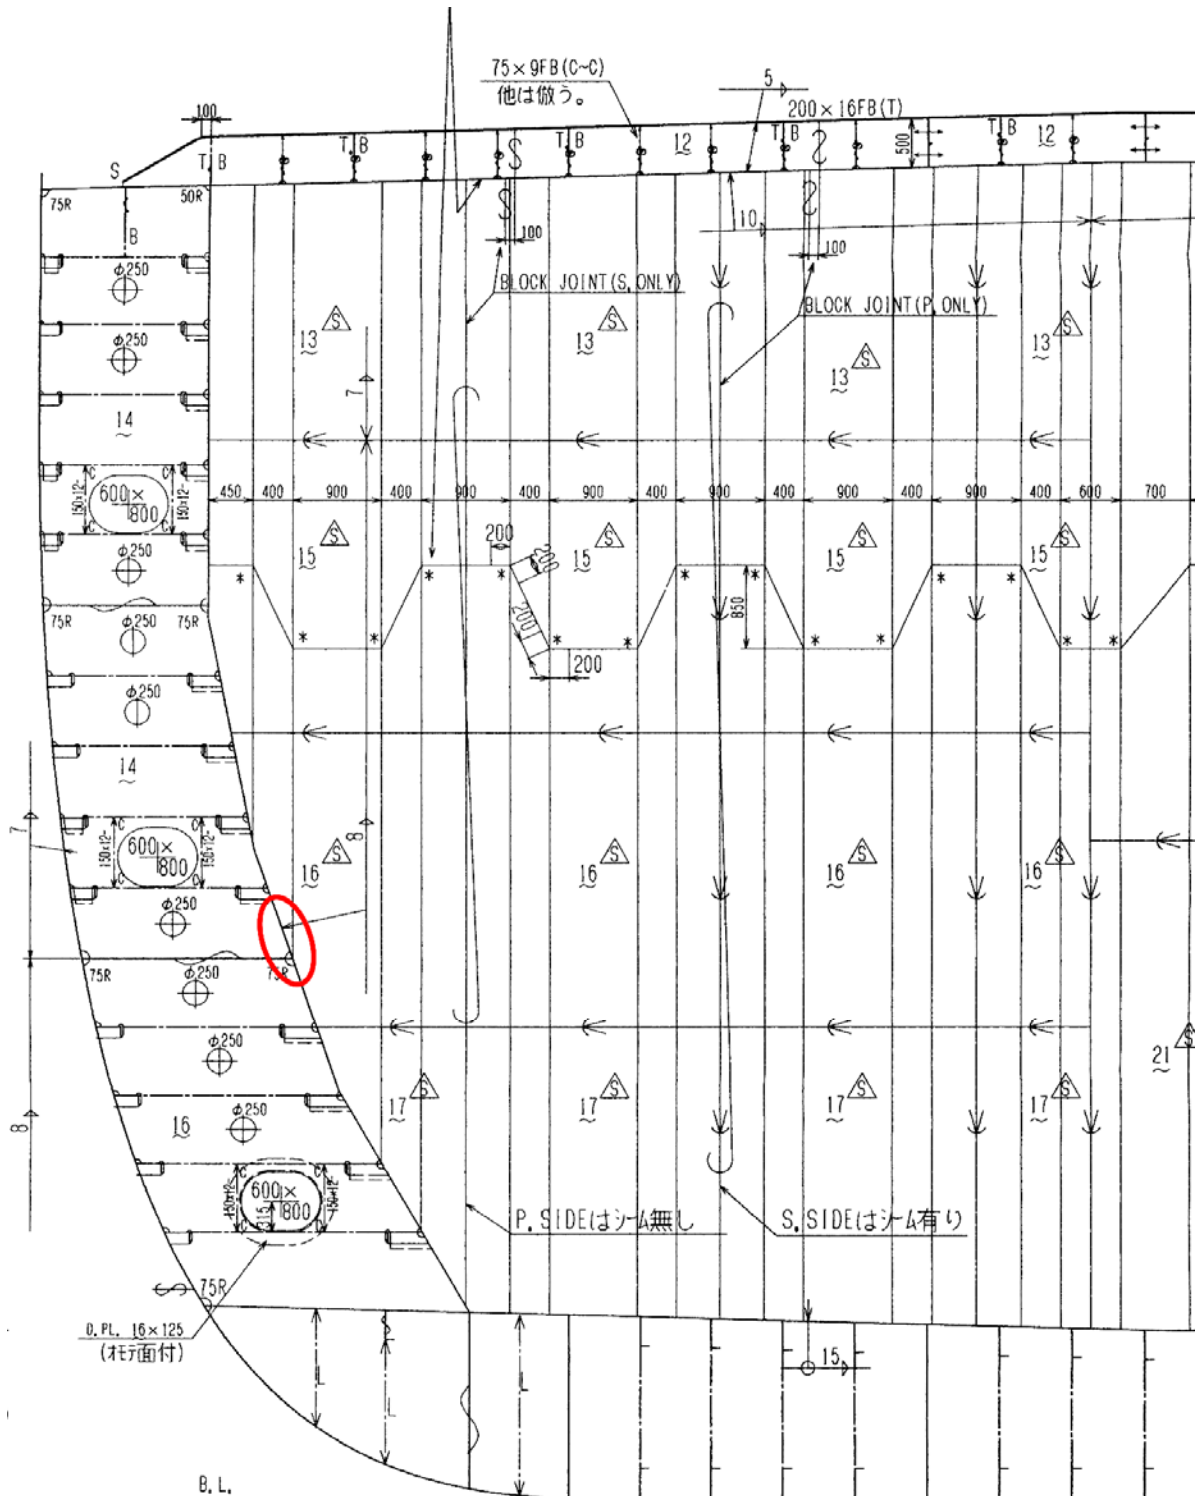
Estructura interna de la zona averiada. Se ha indicado en color rojo la zona donde se produjo la grieta.
